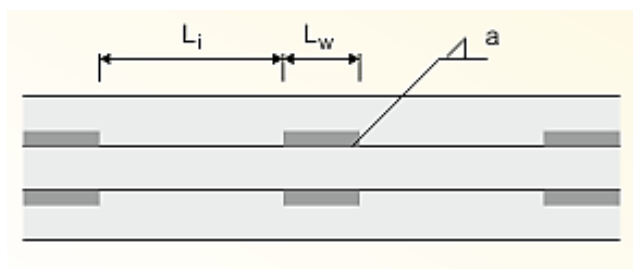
Dimensiones cordón discontinuo. Fuente: Craneway
